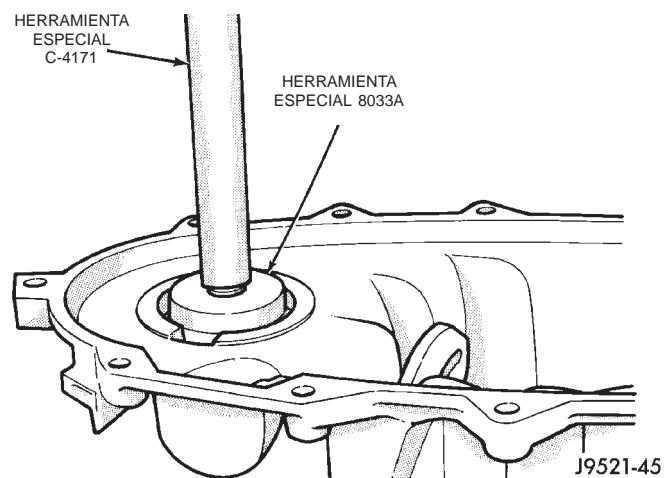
Instalación del cojinete delantero del eje transmisor delantero
